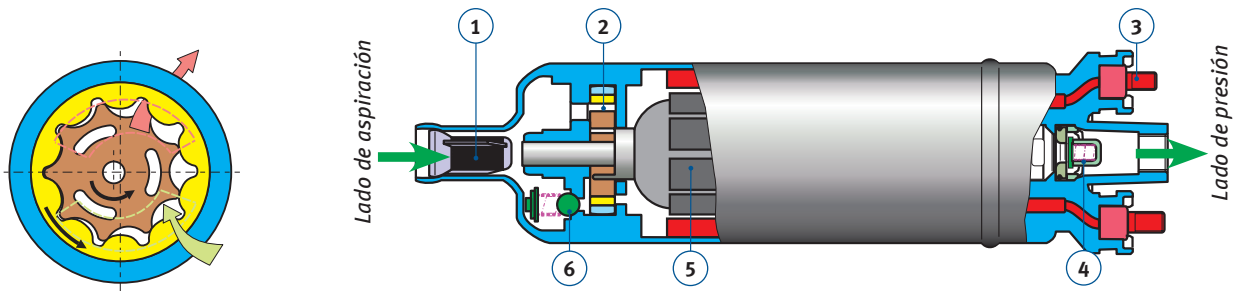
Principio y sección (esquemática) de una bomba de engranaje
